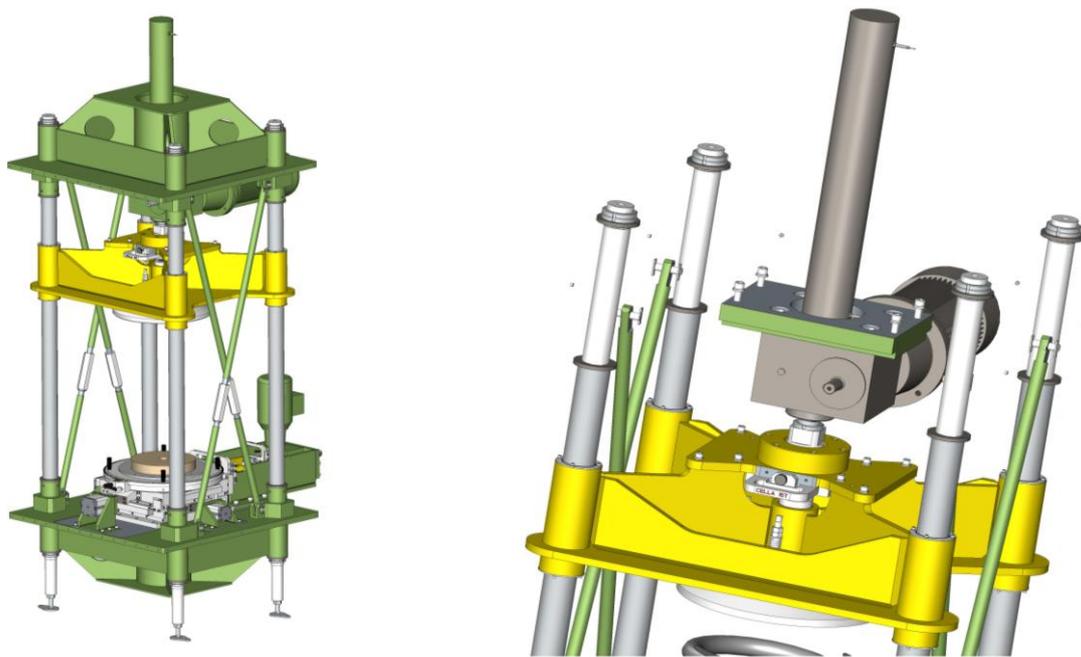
Vista Assieme Pressa Elettromeccanica con Dettaglio Traversa di Spinta
